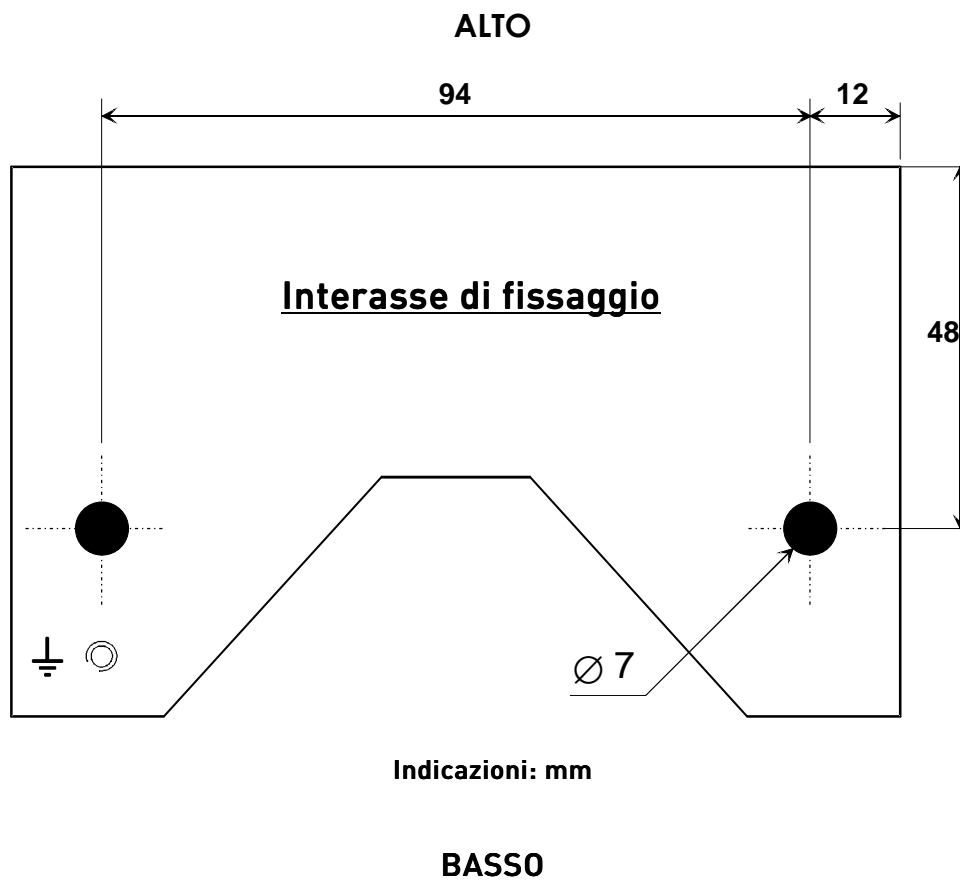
Dimensioni di foratura per il fissaggio del supporto.
